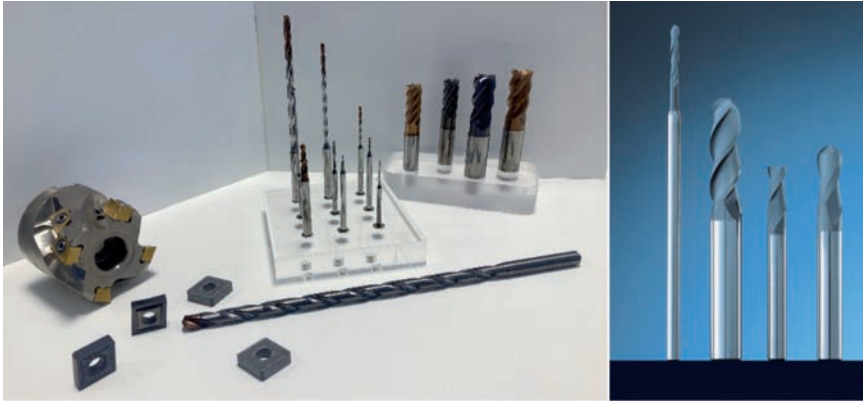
Izda. Herramientas de corte diversas para superlaciones base níquel del motor aeronáutico. Dcha. Herramientas de metal duro recubiertas.
